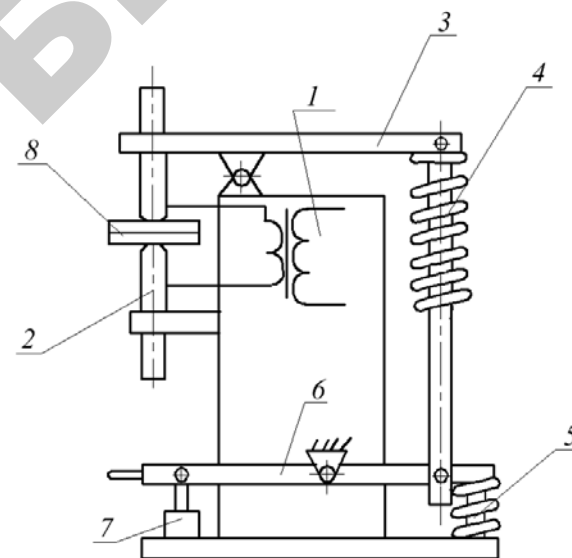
Конструктивная схема машины для электроконтактной точечной сварки:
